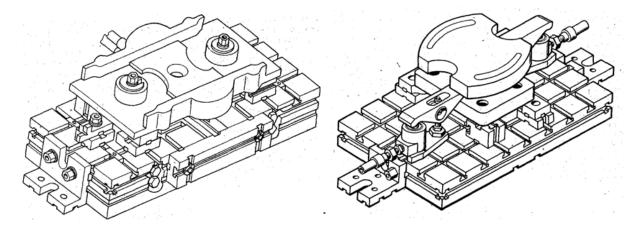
Приспособления, собранные из двух гидроблоков для обработки контура заготовки
